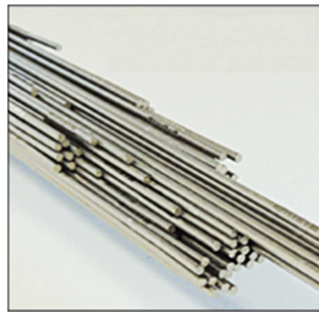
Varetas para soldagem TIG (Adaptado de Daiko Welding, 2015).
